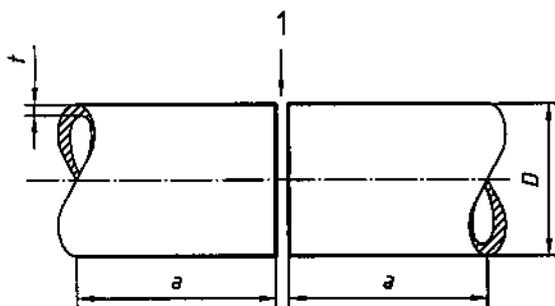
Образец для испытаний стыкового соединения труб с полным проплавлением при сварке
